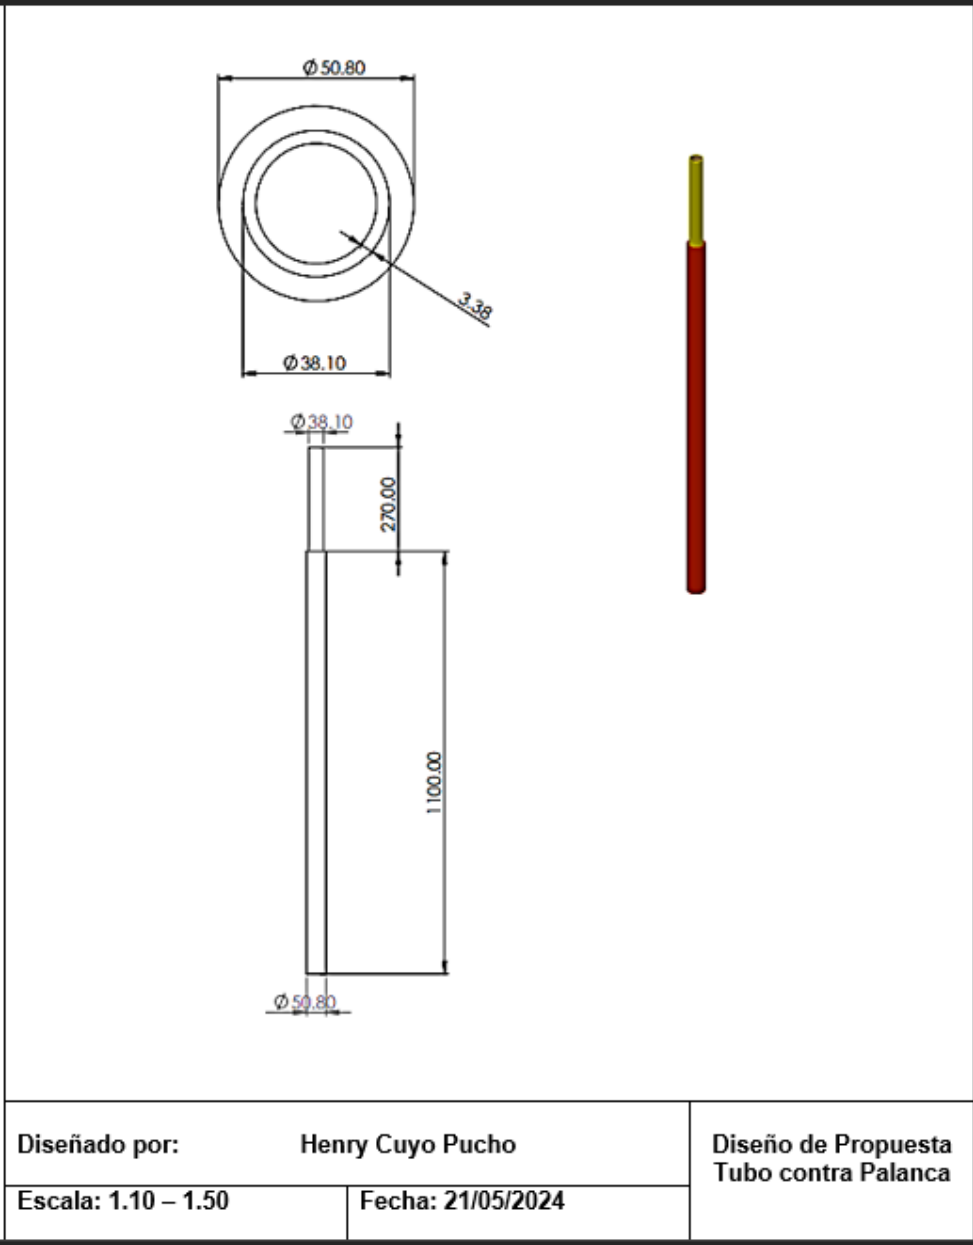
Plano de contra palanca para armado de Covered Base for Barrel – CBB.
